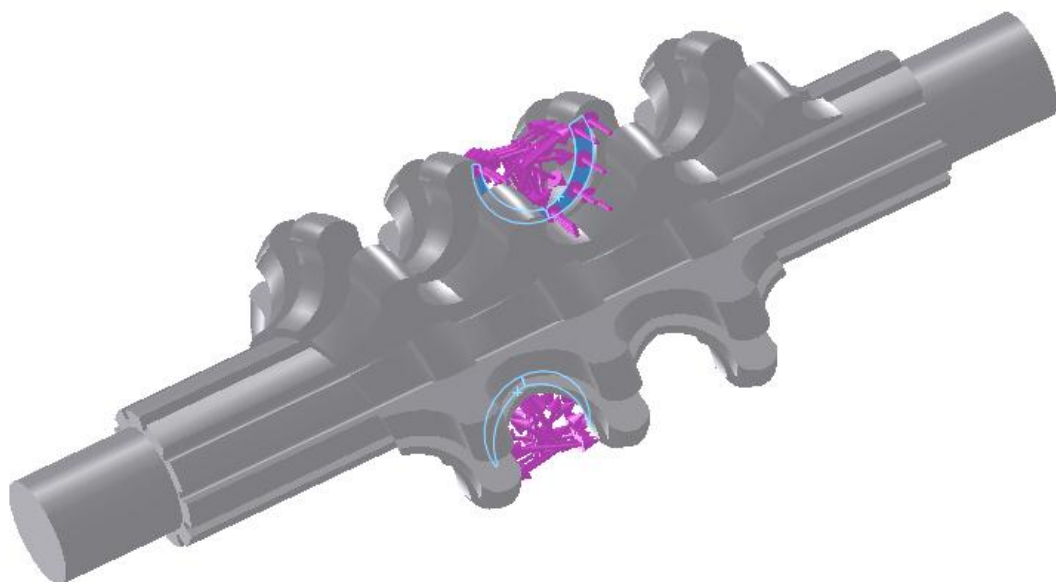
Формування навантаження профільної черв'ячної фрези радіальними та тангенціальними силами різання при одночасному обробленні ДВОХ ЗАГОТОВОК
